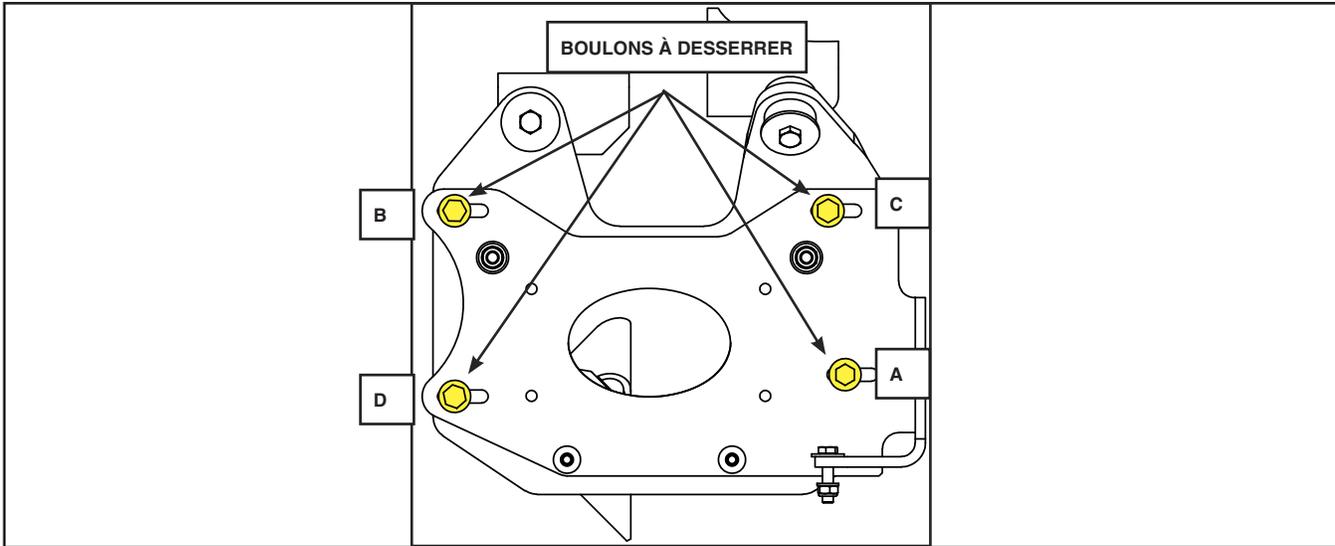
Boulons de retenue de la plaque du compresseur et séquence de serrage
